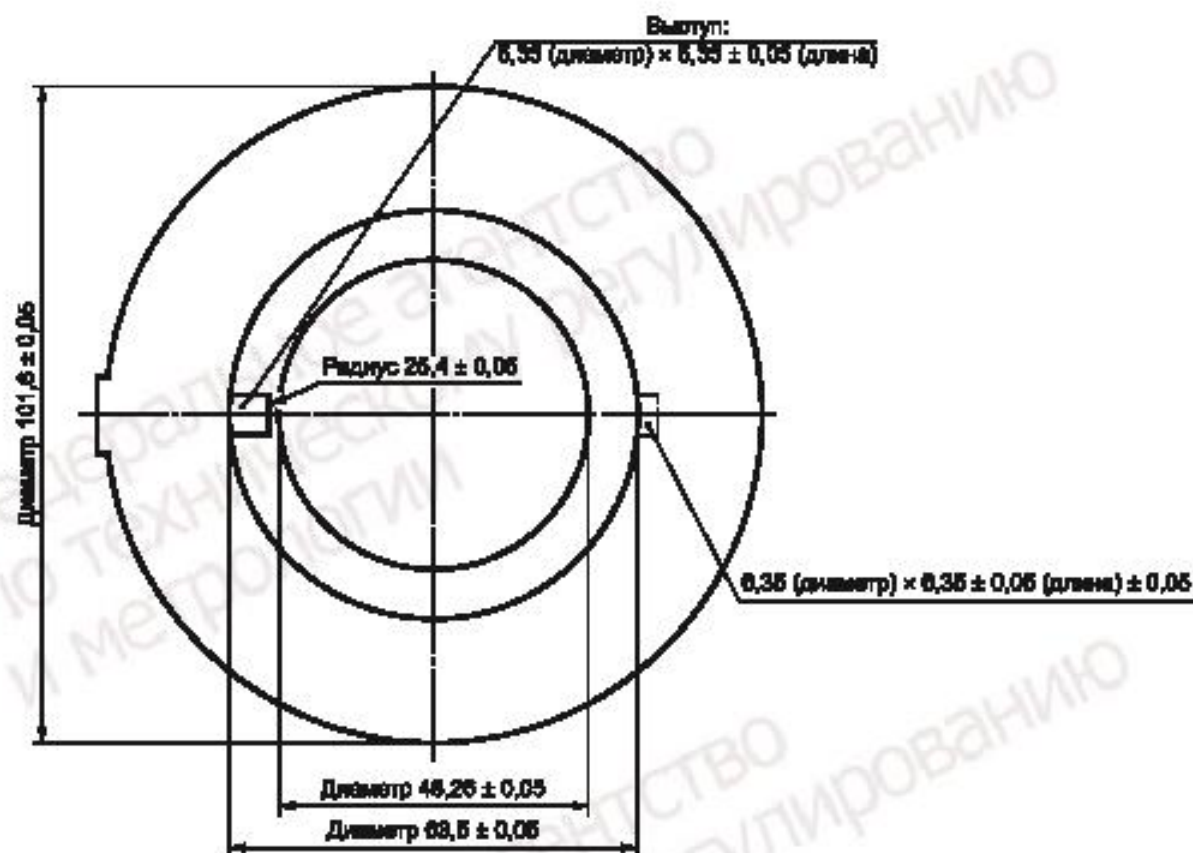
Форма из силиконовой резины (вид сверху), размеры указаны в миллиметрах
